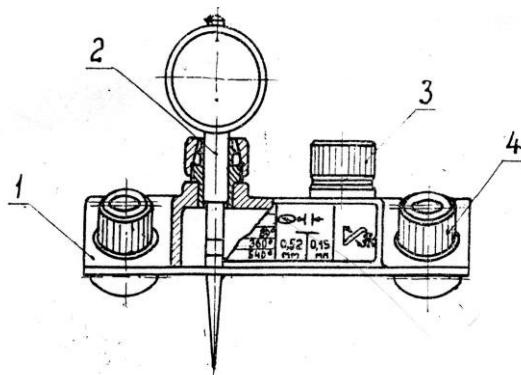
Пристрій індикаторний для перевірки зазорів :
